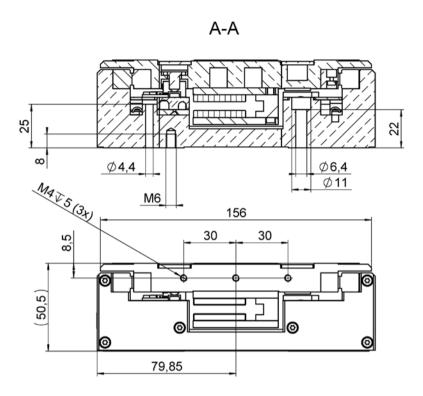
Abmessungen des V-551.2D: Schnitt A und Seitenansicht
